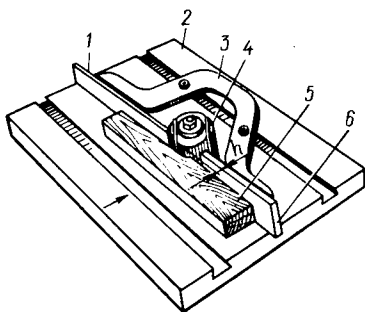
Обработка прямолинейной кромки на фрезерном станке:
